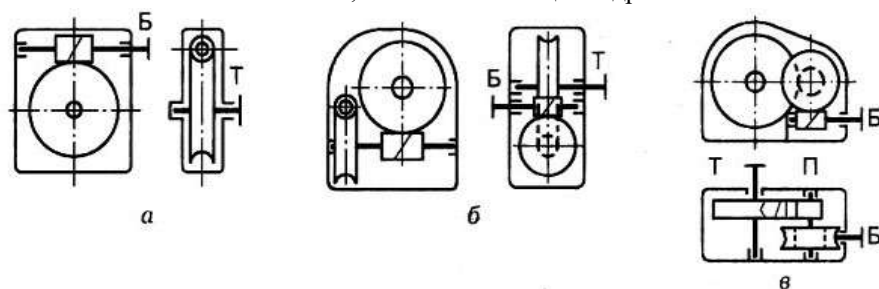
Схемы червячных редукторов: а — одноступенчатый; б — двухступенчатый; в — червячно-цилиндрический
